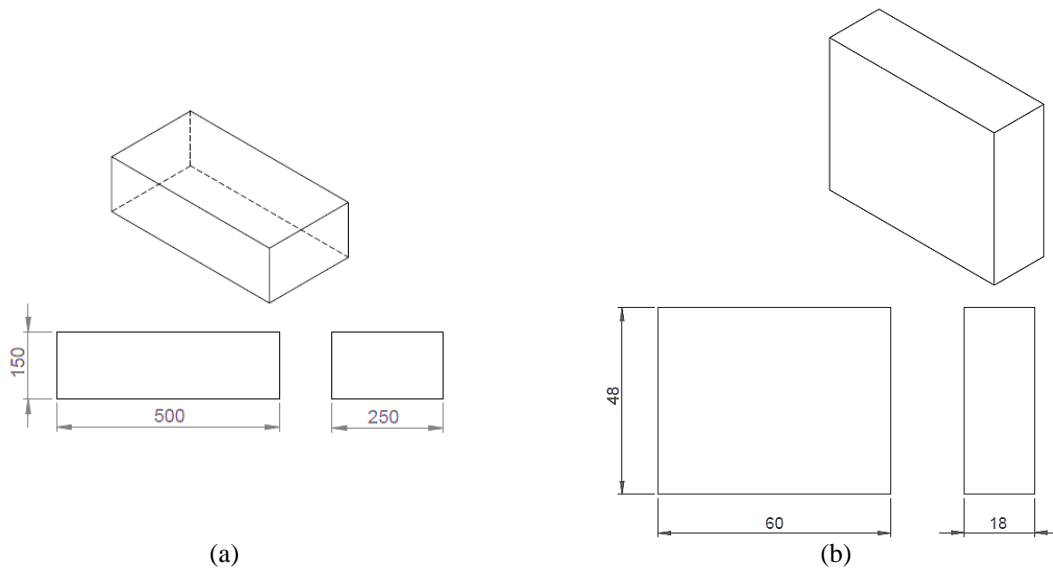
Dimensões (em mm) do bloco de aço padrão fresado nos experimentos (a) e dimensões (em mm) das amostras fabricadas a partir do bloco padrão
